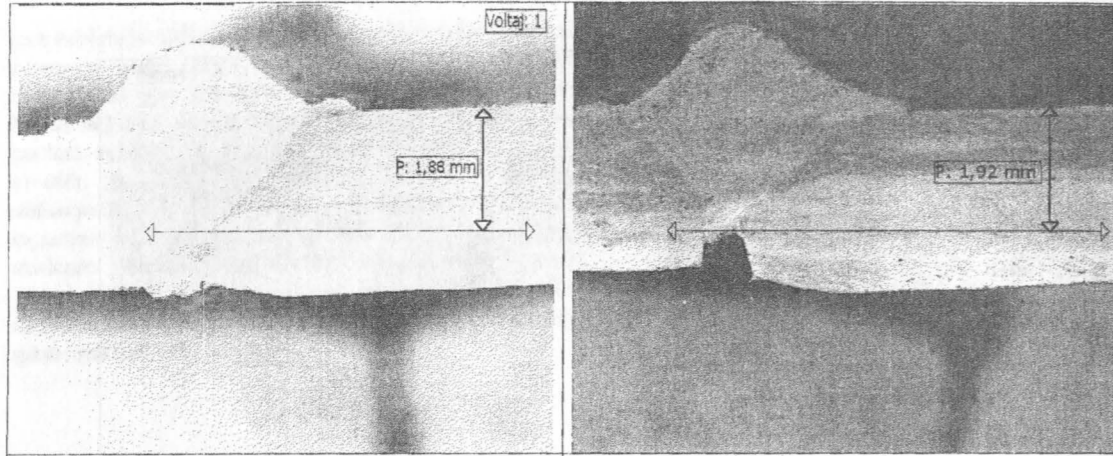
95 Amper kaynak akımı makroyapı fotoğrafı (X10)
